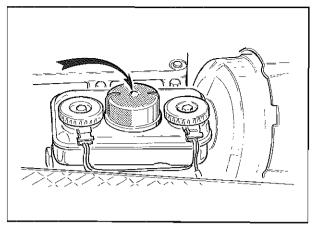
Tappo serbatolo impianto frenante Brake system tank cap
